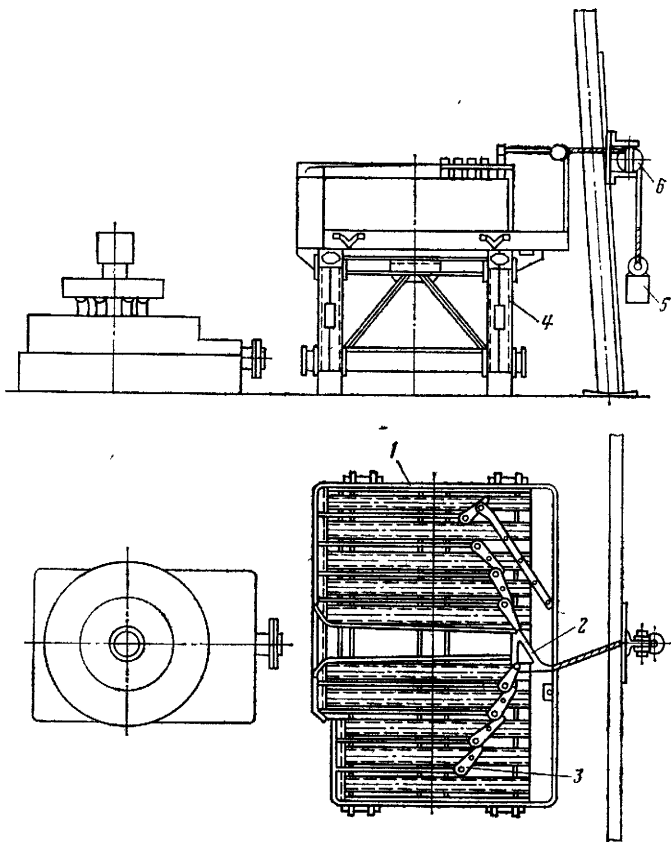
Приспособление для автоматической установки свечей АУС-3
